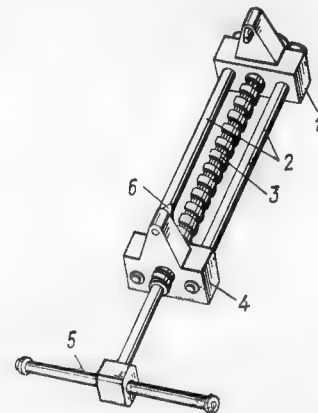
1 — упор нижний; 2 — направляющие; 3 — винт; 4 — упор верхний; 5 — ручка; 6 — палец конический
